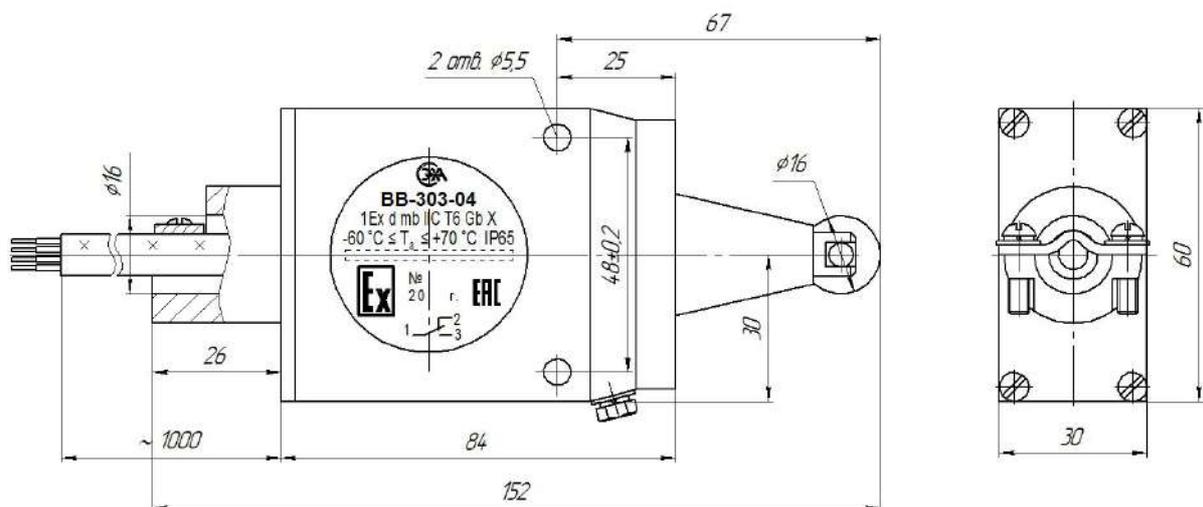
Габаритные и установочные размеры выключателей BB-303...BB-303-02
